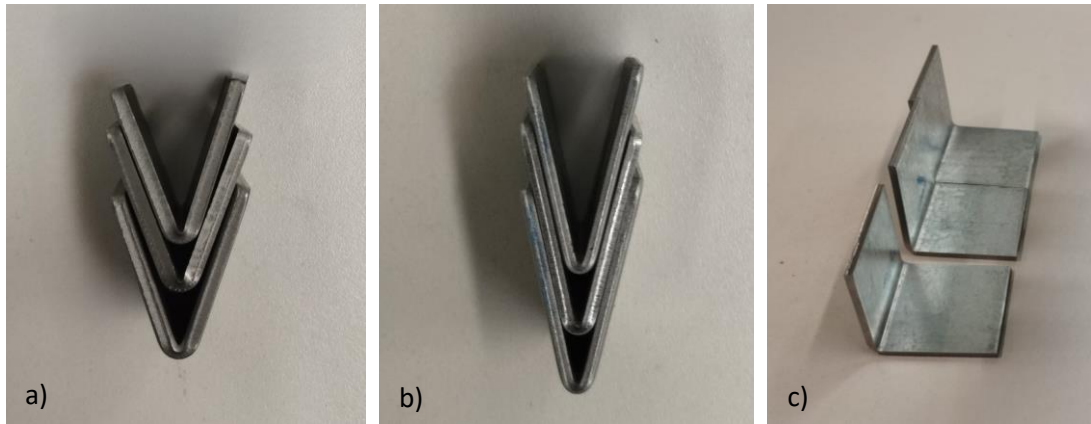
Provetes após o ensaio de dobragem: a) HR700LA; b) CR340LA; c) DP800
